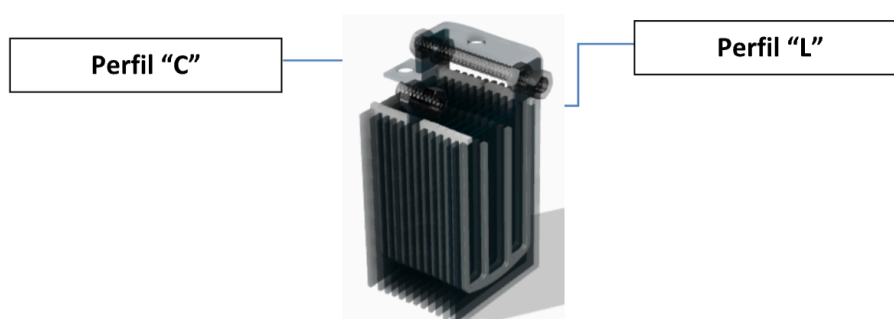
Sandwich con perfil "C" y perfil "L" sujetado con tuercas y arandelas
